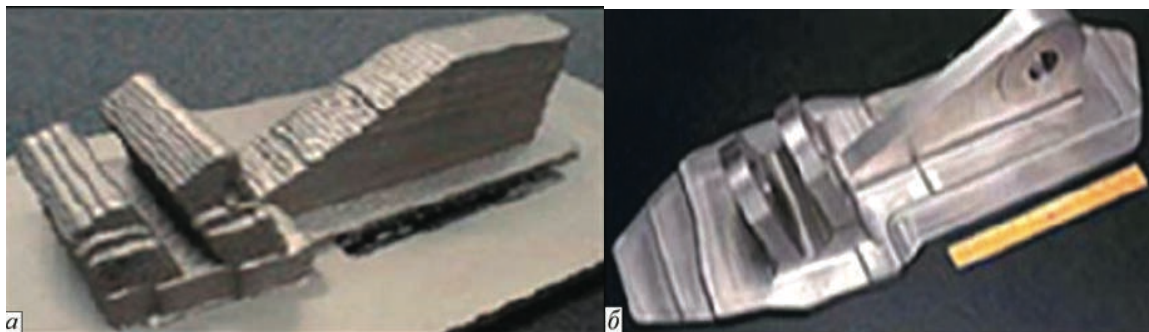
Заготовка (а) детали (б) выполненная способом WFLB (лазерная наплавка проволоки) [6]
